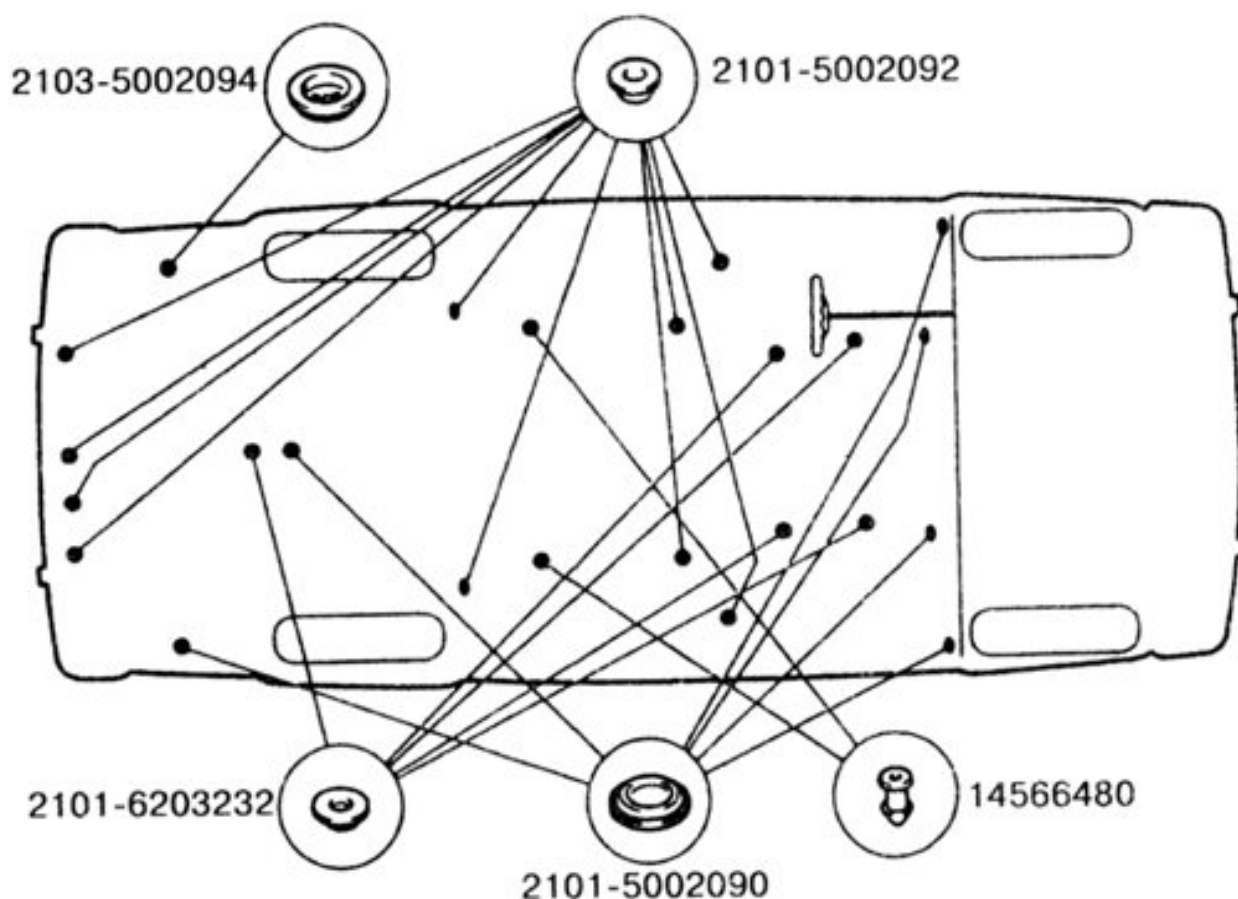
Схема установки заглушек на кузове ВАЗ-2106
